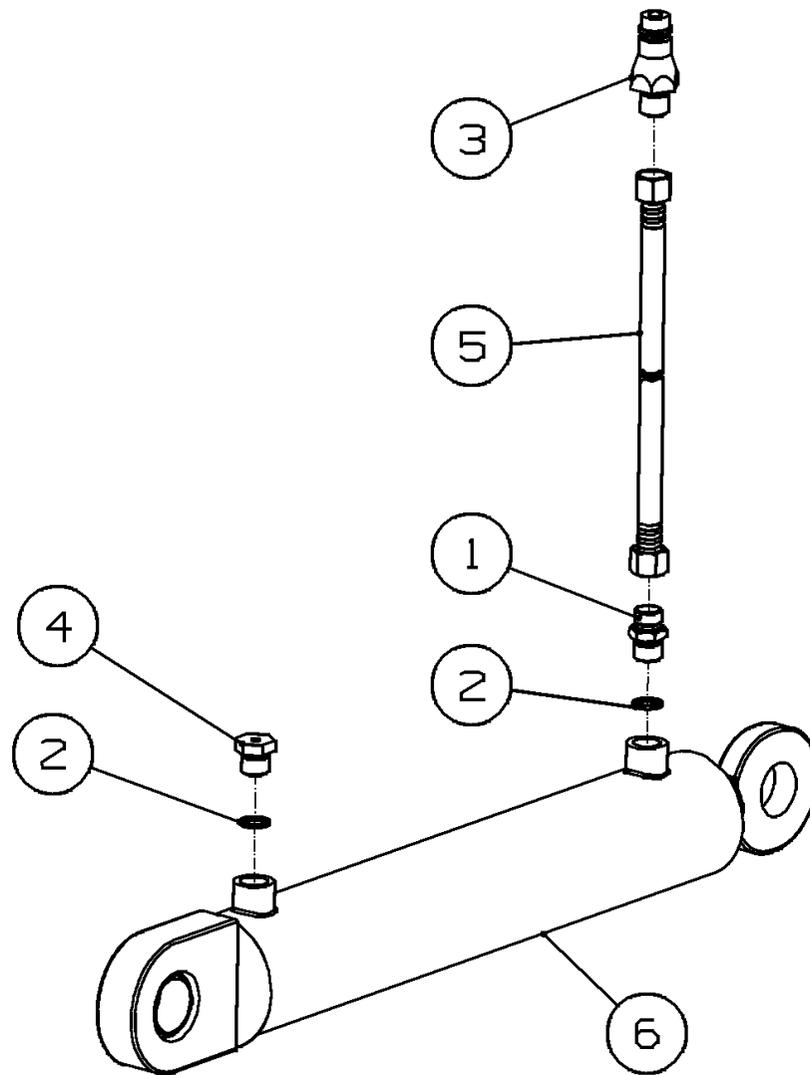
КРК - 2.4.00.210 Гидроцилиндр
